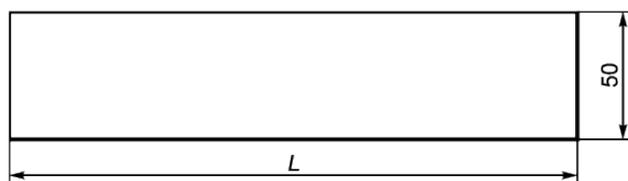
Образец для испытаний типа 1 (прямоугольный)
